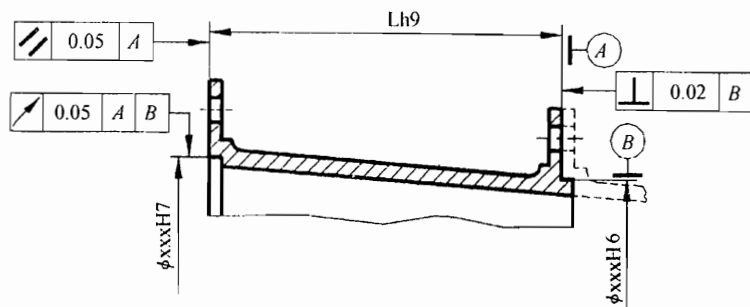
周向安装边尺寸公差和形位公差示意图
